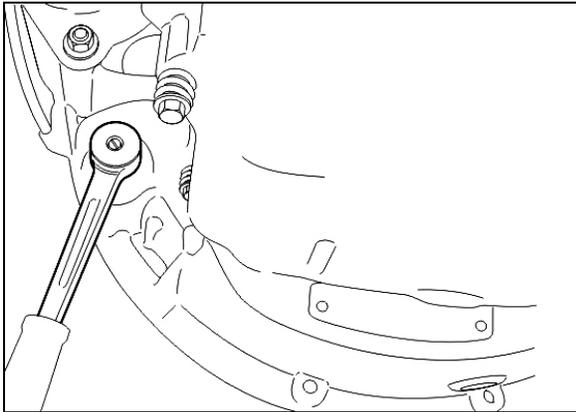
POSICIÓN DE GIRO DEL MOTOR VOLVO
